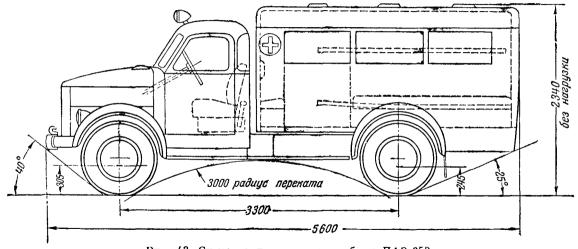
Схема санитарного автомобиля ПАЗ-653.
